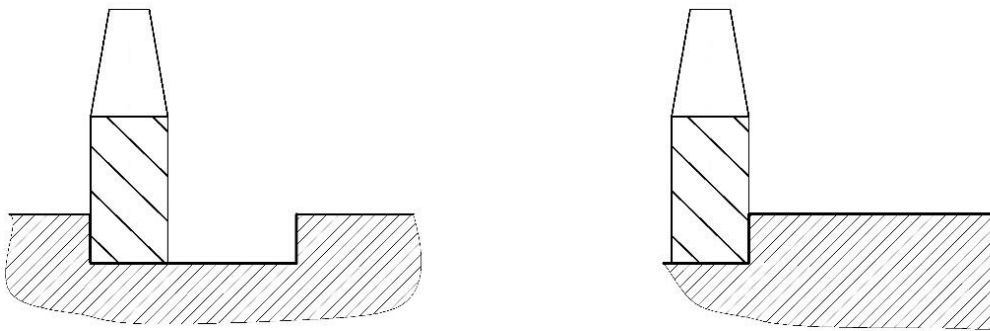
Попередня обробка пазу кінцевою фрезою
